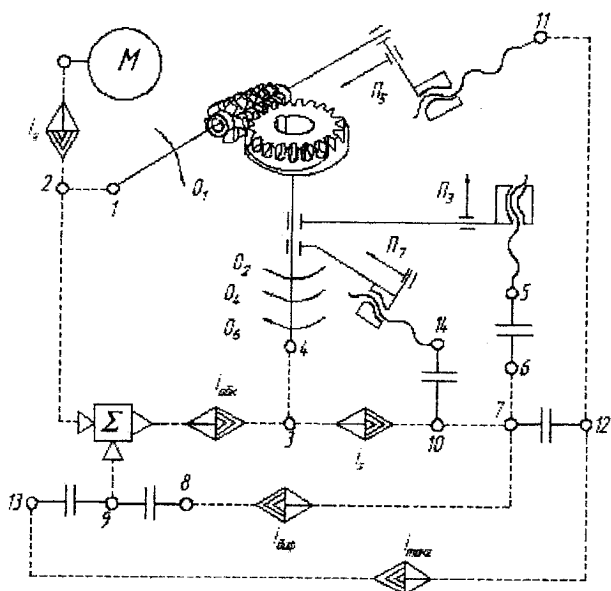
Кінематична структура універсального зубофрезерного верстата
